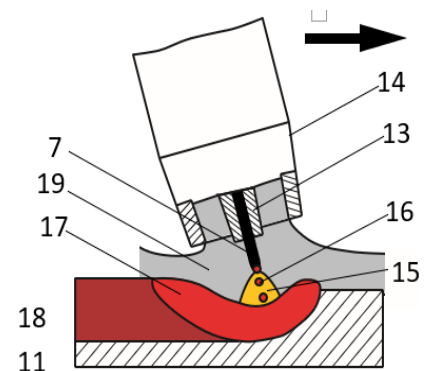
Equipement d'un poste de travail : Soudure TIG.
